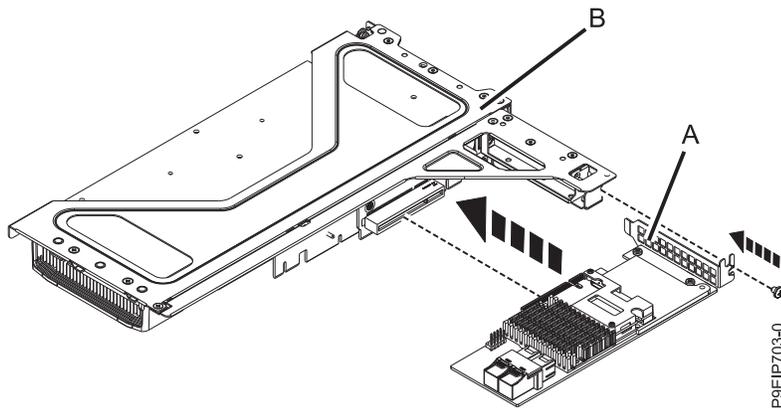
Inserción de un adaptador en la posición 4 de la tarjeta de expansión
